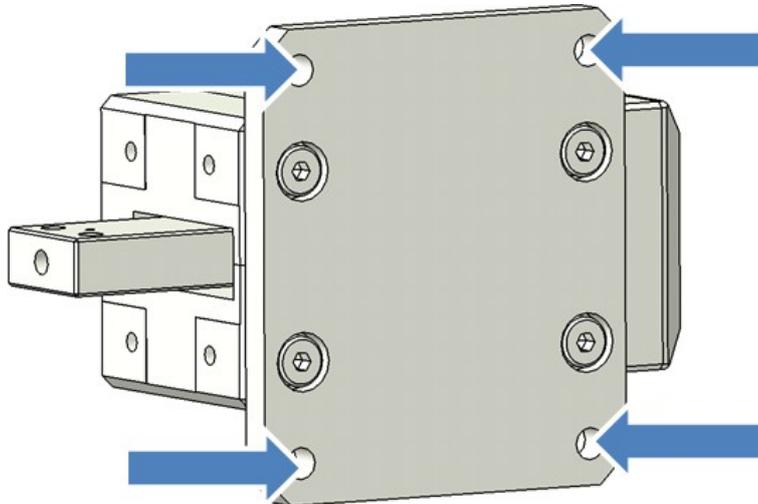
Montageflansch A: Position der verwendeten Montagebohrungen
